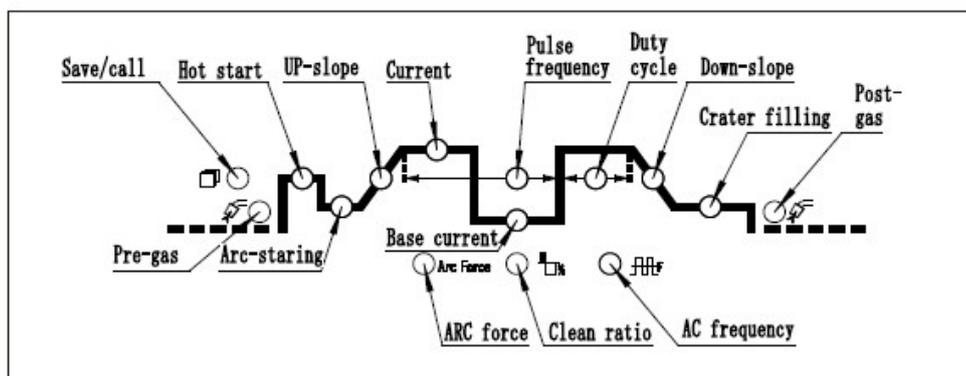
Схема регулировки сварочных параметров
